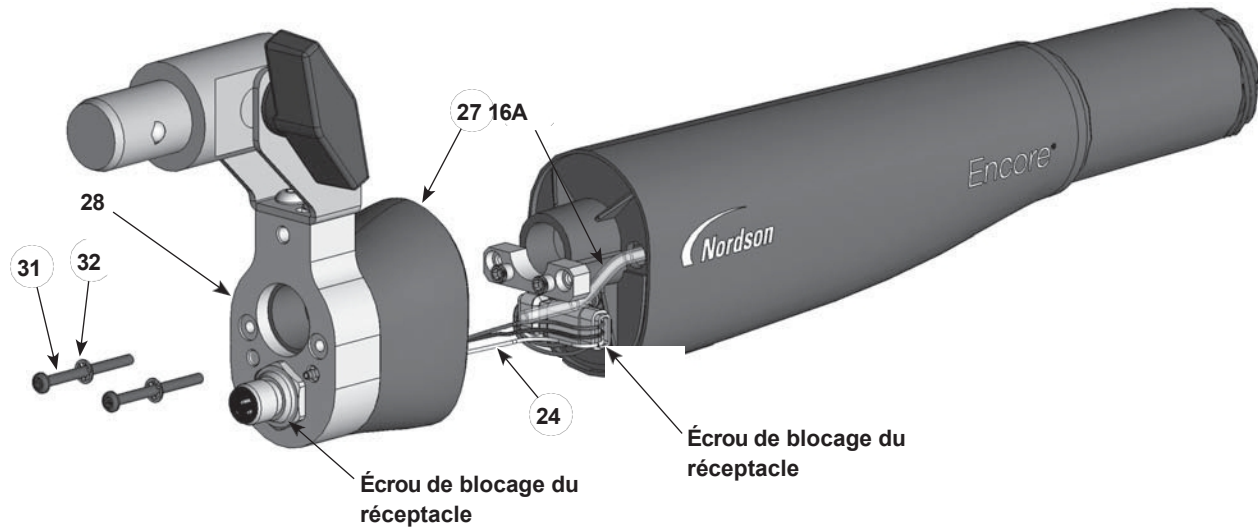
Démontage de l'embout du pistolet - Remplacement du tube à poudre
